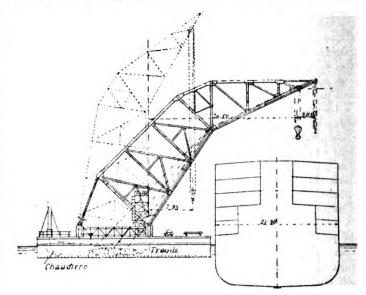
Gru galleggiante da 150 tonn. dei Cantieri di Kawasaki - Elevazione.
